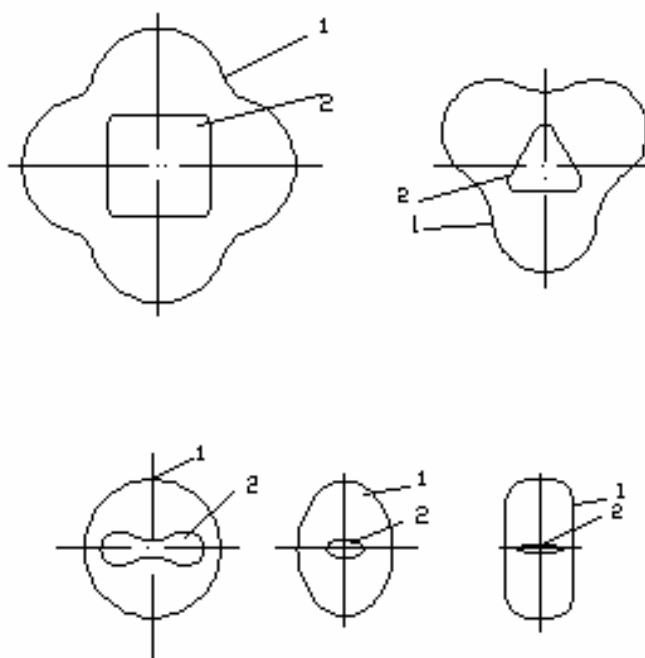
Формы заготовок при вытяжке глубоких коробчатых деталей различного сечения
